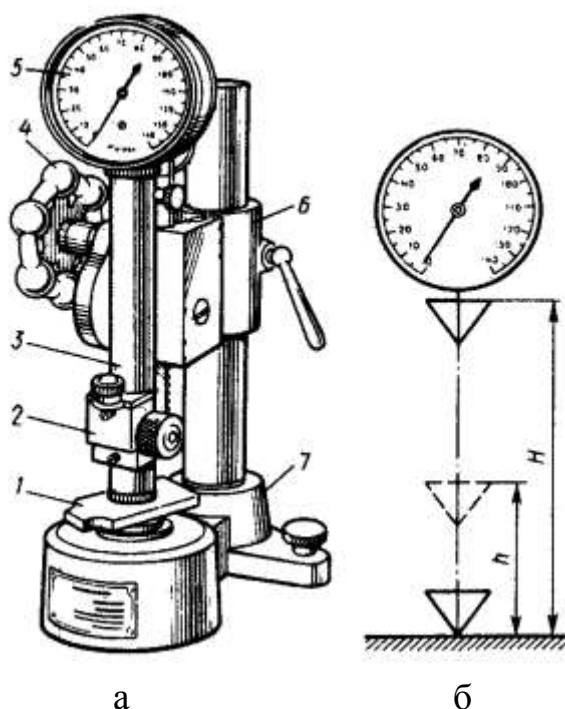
Прилад для визначення твердості за методом Шора: а – загальний вигляд приладу; б – схема визначення твердості; 1 – деталь; 2 – пристрій для повернення бойка у вихідний стан; 3 – трубка; 4 – рукоятка; 5 – індикатор; 6 – затиск; 7 – станина
